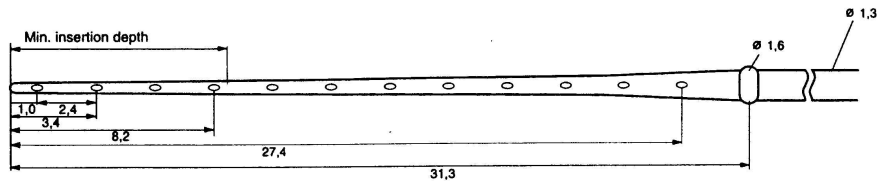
Dimensiones de la guía portaelectrodos estándar del implante Combi40+.
